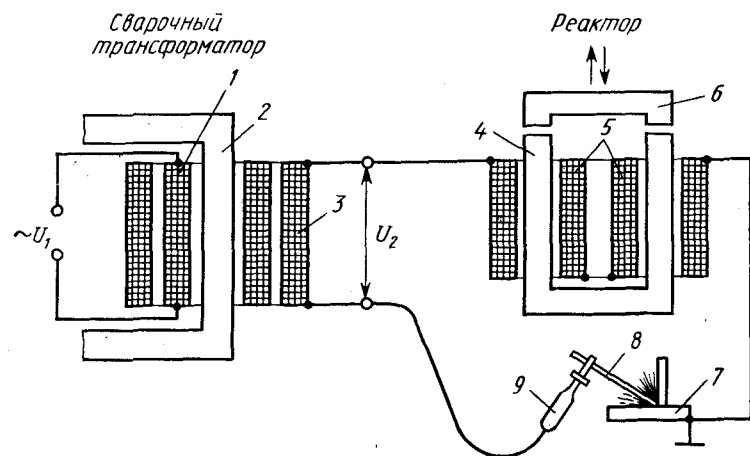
Принципиальная схема устройства и работы сварочного трансформатора
